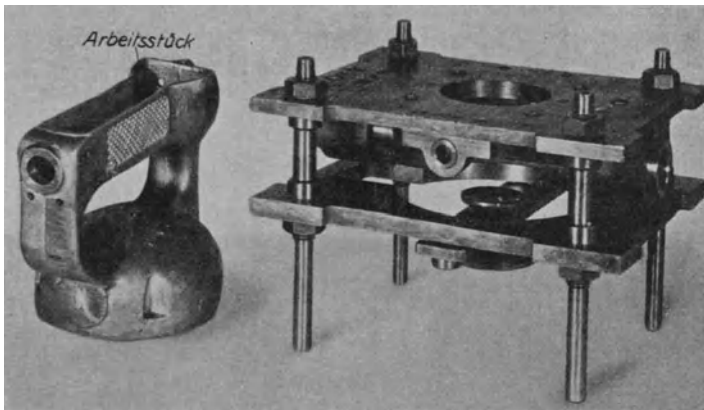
Bohrvorrichtung für die Haube der elektrischen Bohrmaschine.
